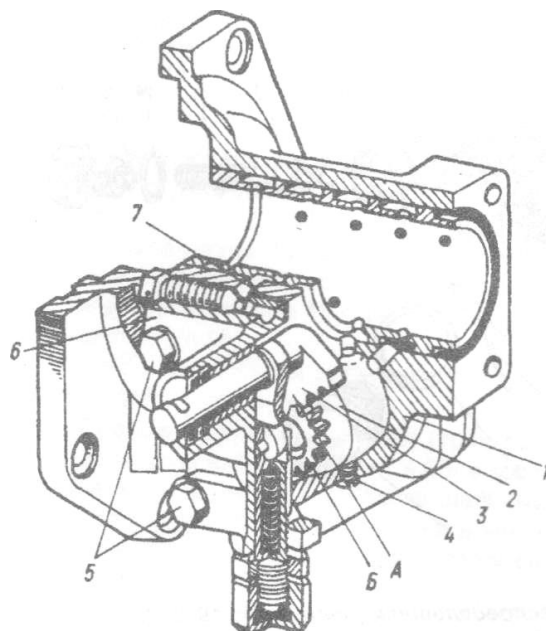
Складання гідророзподільника: 1 — корпус; 2 — золотник; 3 — сектор; 4 — гвинт; 5 — болт; 6 — клапанний механізм; 7 — прокладка; А, Б — мітка
